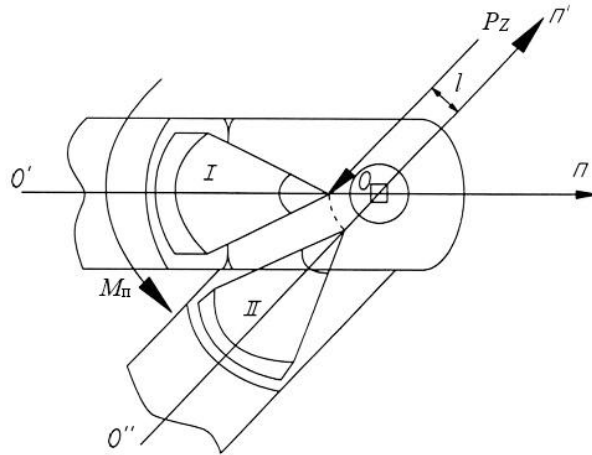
Схема функционирования устройства для крепления и автоматической самоустановки резца
